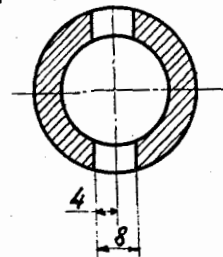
Приспособление для опрессовки транзистора на радиаторе.
